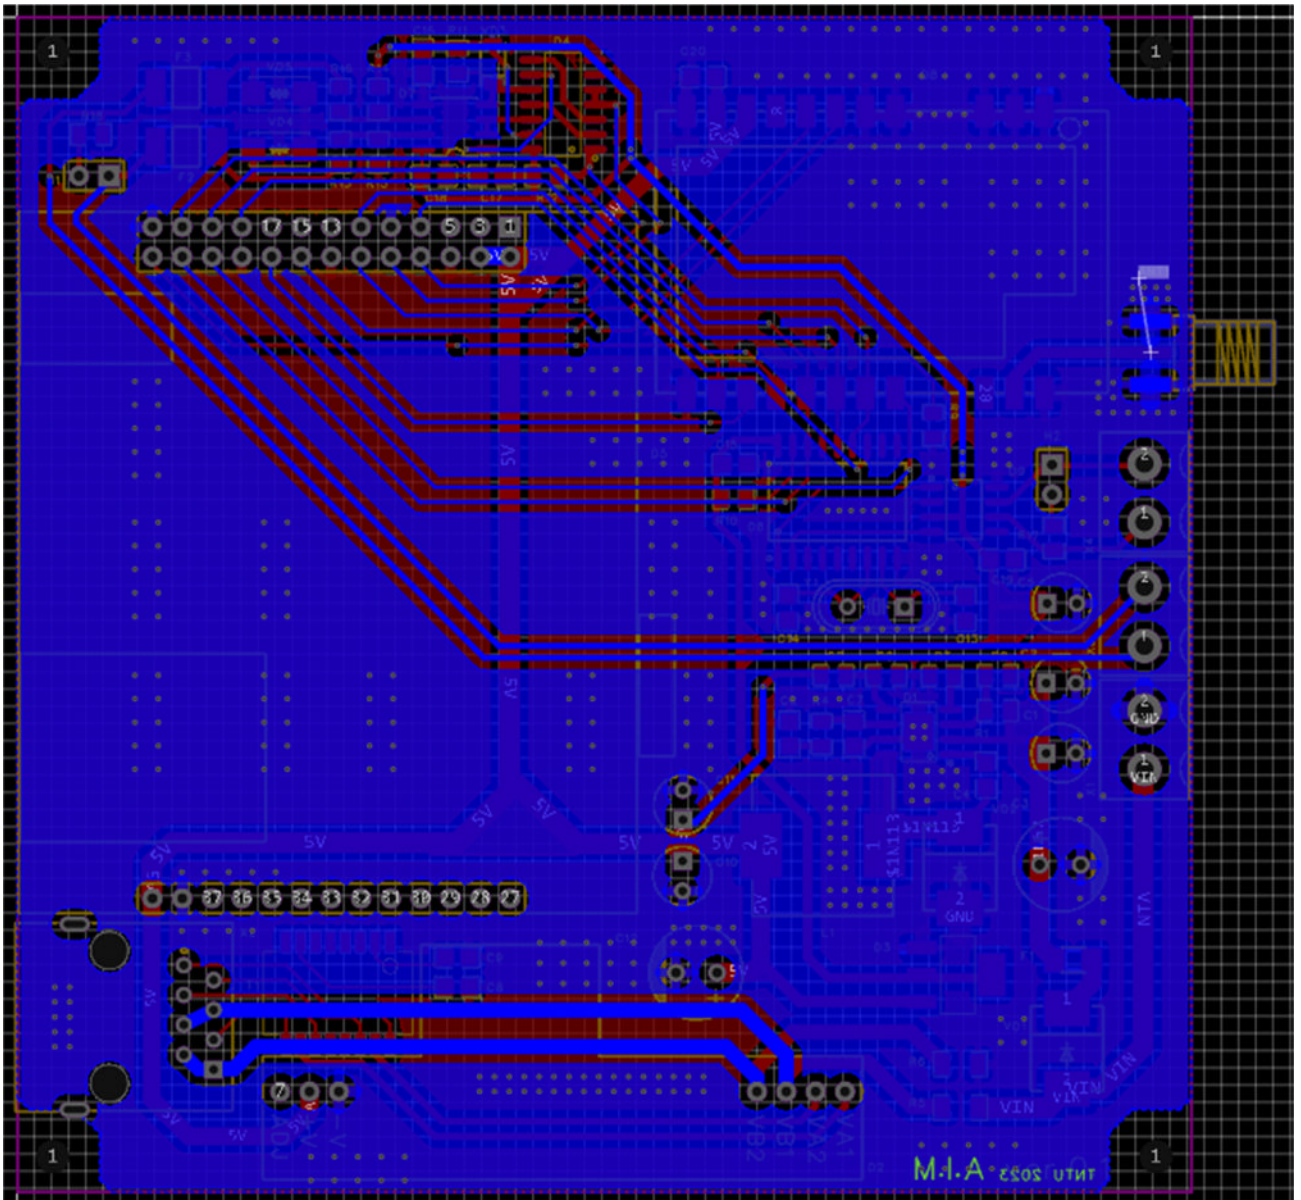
Шар Bottom Layer друкованої плати
